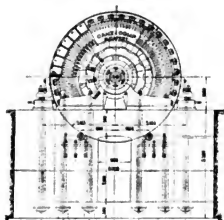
Generatorseite einer 6000 PS-Maschinengruppe Manojlovac.
